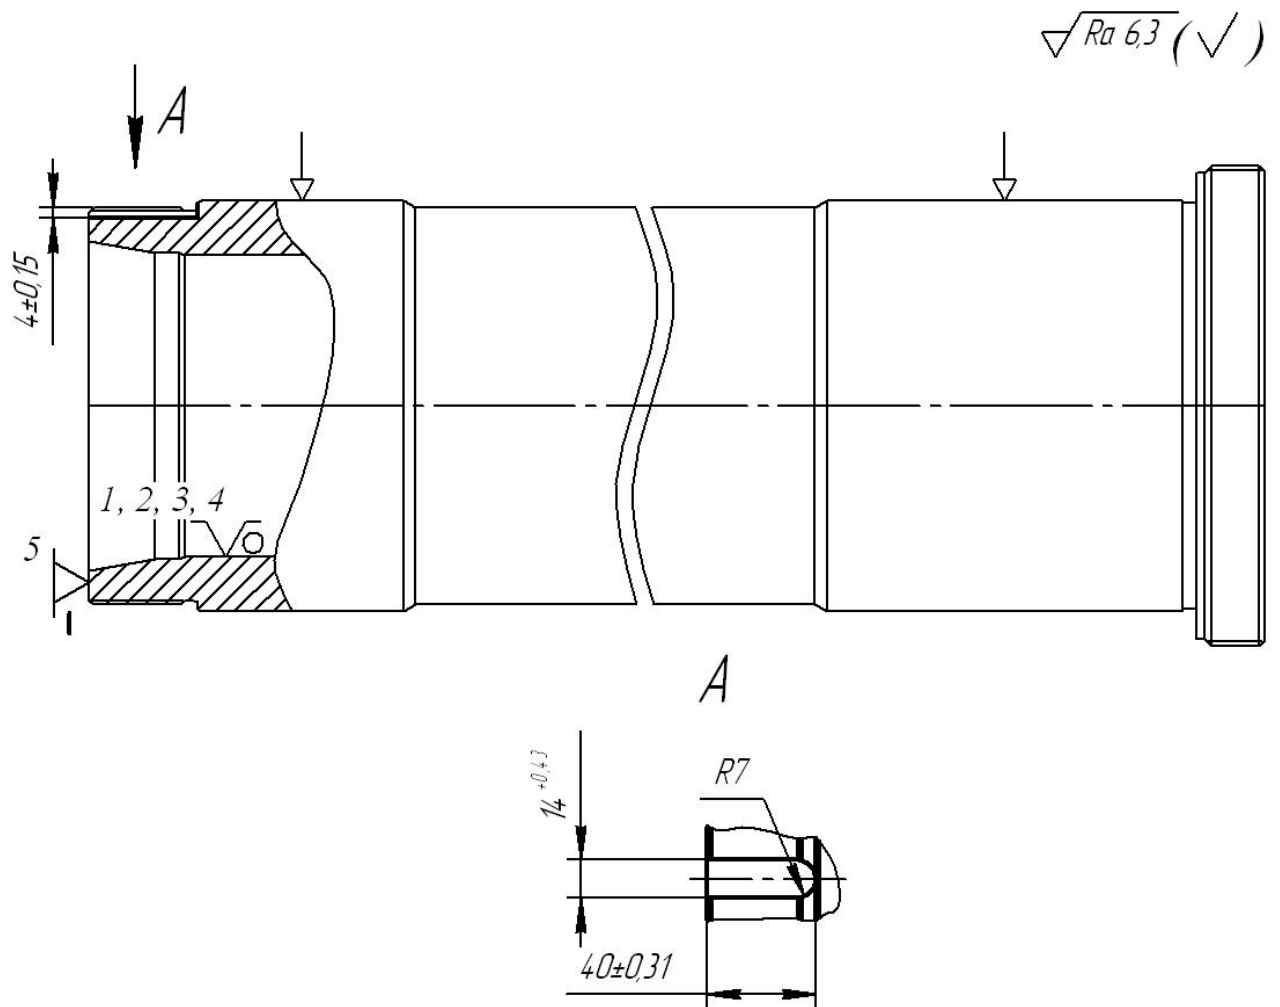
Альтернативна схема базування заготовки на операції фрезерній з ЧПК 040
